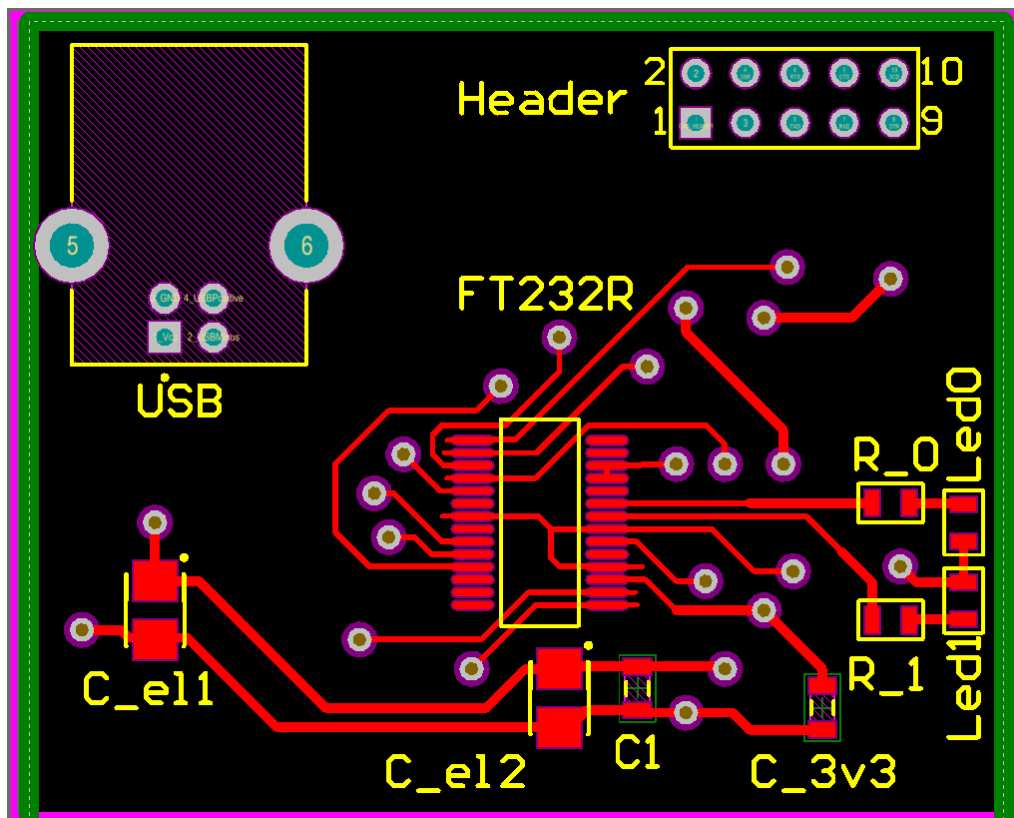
Capa superior del PCB diseñado en Altium Designer.
